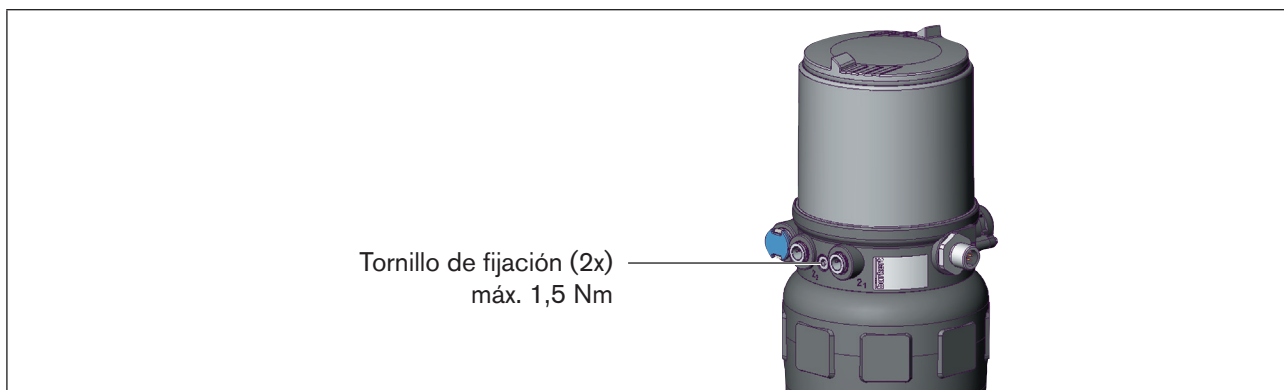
Montaje del posicionador, series 26xx y 27xx
